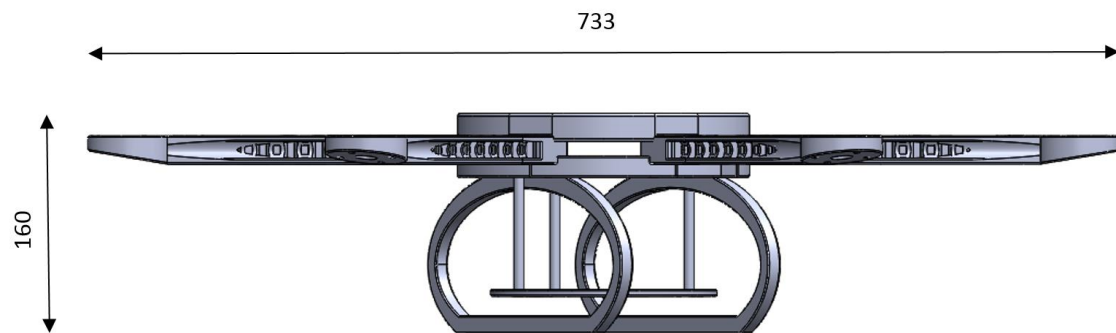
Diseño del soporte para accesorios en SolidWorks.
